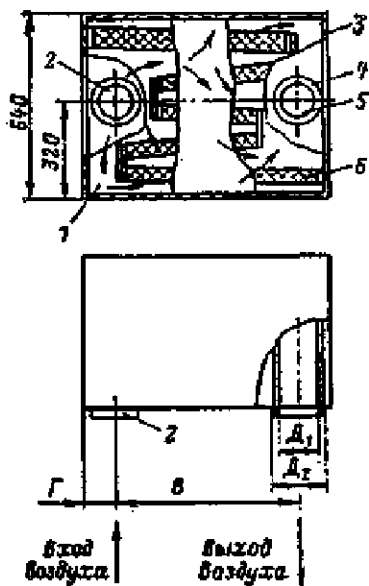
Фильтр грубой очистки ФГ: 1 - форкамера; 2 - входное отверстие; 3 - корпус; 4 - выходное отверстие; 5 - уплотнительное кольцо; 6 - фильтрующий элемент.
